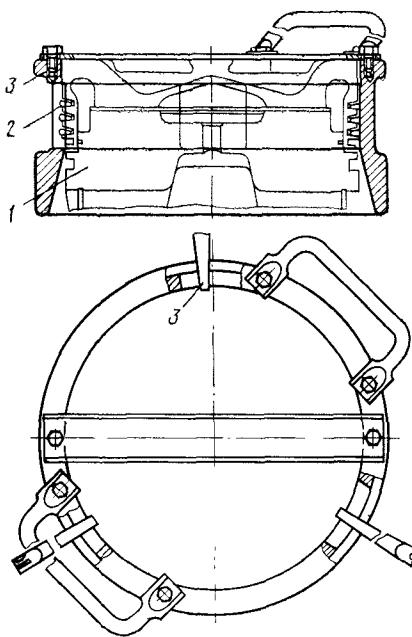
Приспособление для замера зазоров между канавками поршня и компрессионными кольцами:
